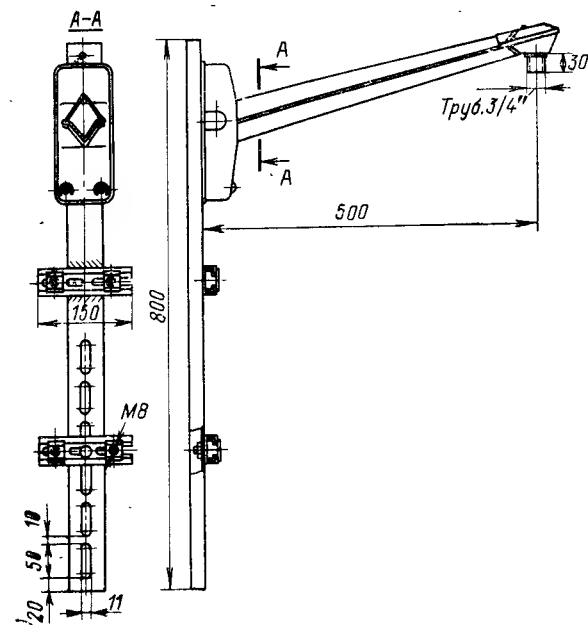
Кронштейн КР7-м для установки светильника с лампой ДРЛ на стене.
